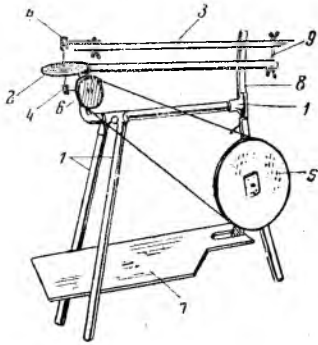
Ножной выпиловочный станок: 1—станина; 2—столик; 3—качающаяся рама; 4—барашки; 5—маховик; 6—шкив с кривошипным механизмом; 7—педаль; 8—стойка станины; 9—пружина
